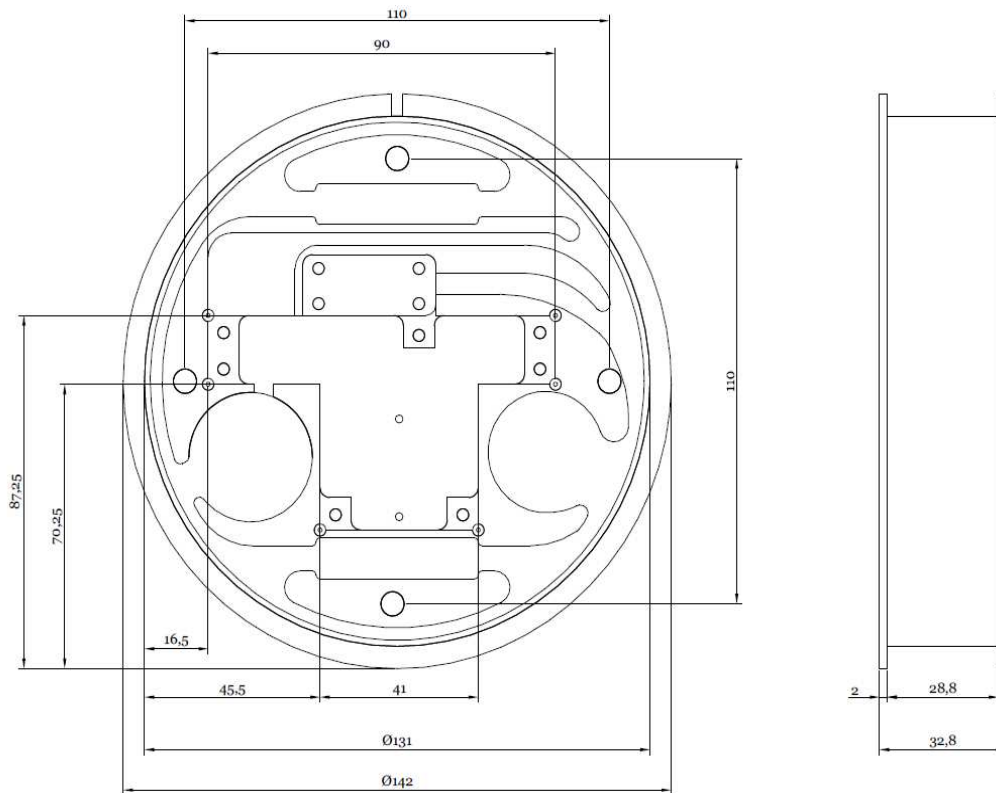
Desenho do carretel da bobina de fibra óptica – Vista de topo
